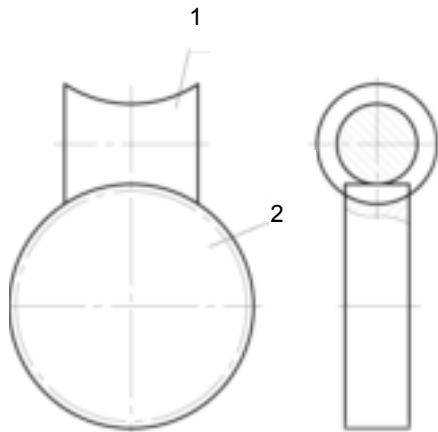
Схема глобоидной передачи с цилиндрическим колесом:
